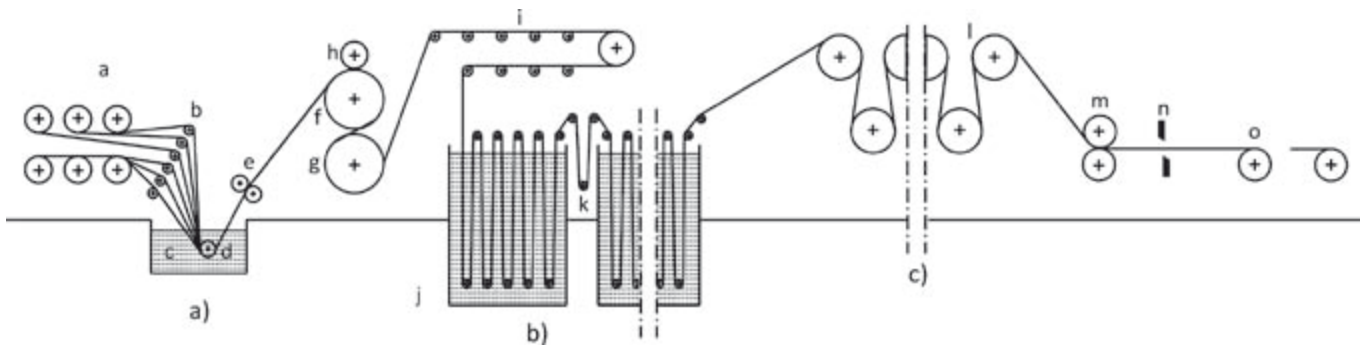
Kontinuierliche Fertigung technischer Vulkanfaser [5]
